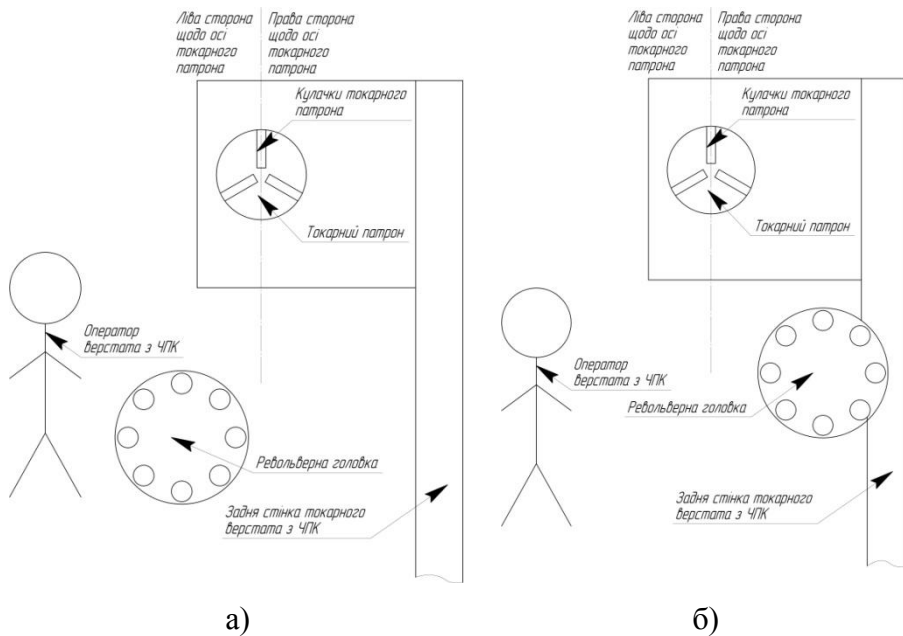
Схема розміщення револьверної головки токарного верстата з ЧПК: а) зліва; б) справа
